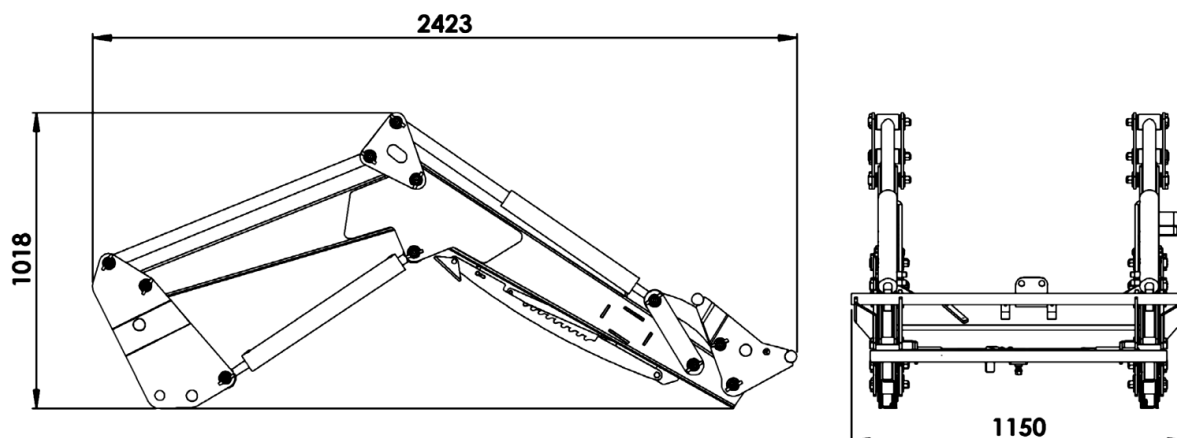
Размеры погрузчика подготовленного для транспортировки
